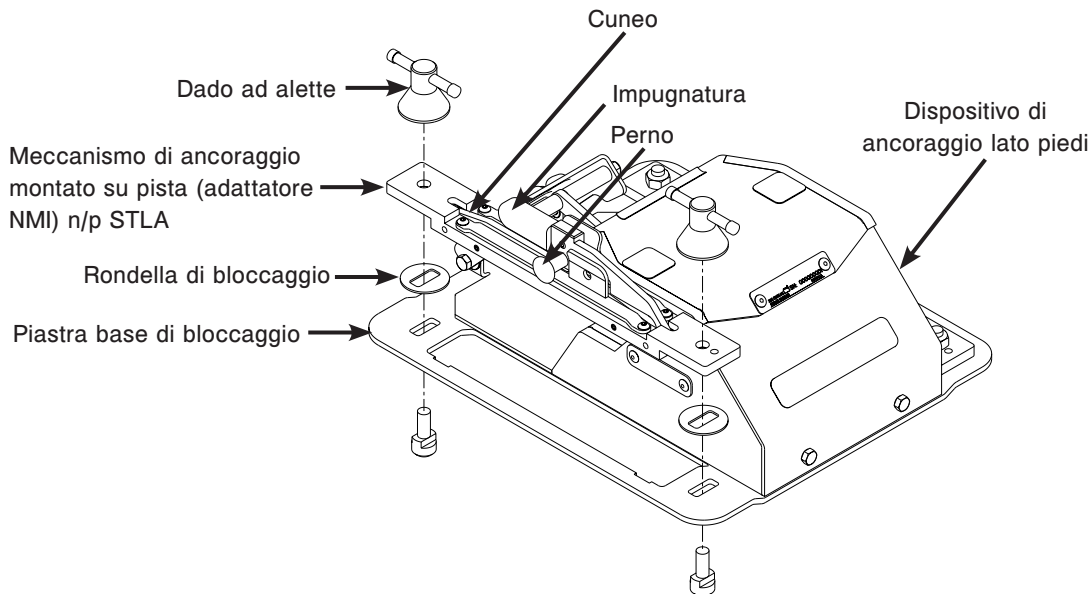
Assemblare il dispositivo di ancoraggio per lato piedi
